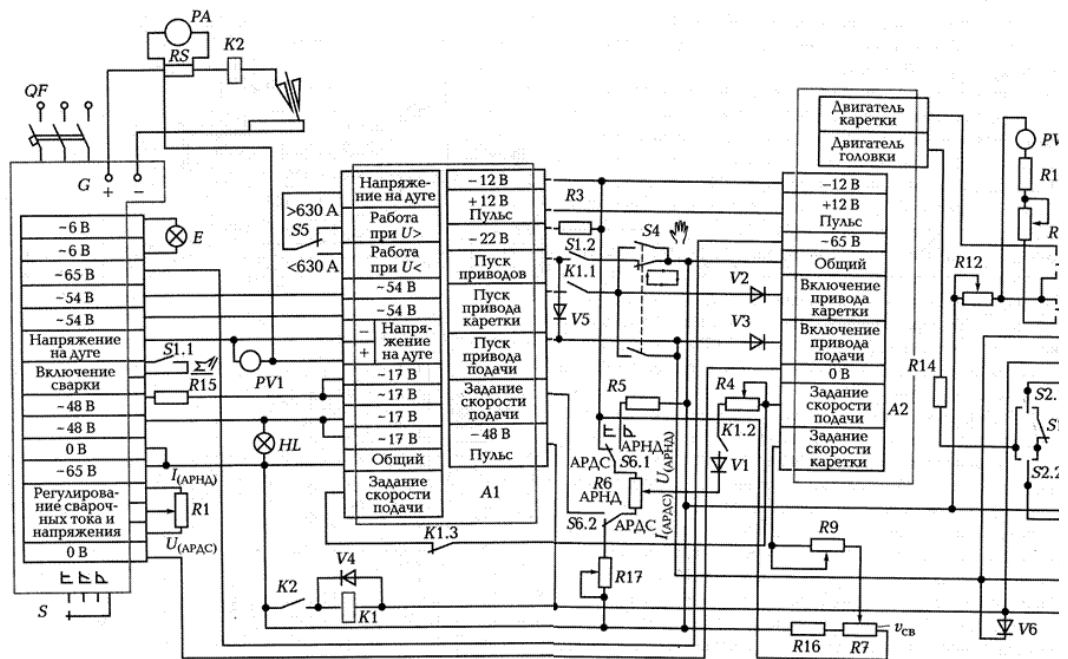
Принципиальная схема сварочного трактора АДФ-1202
